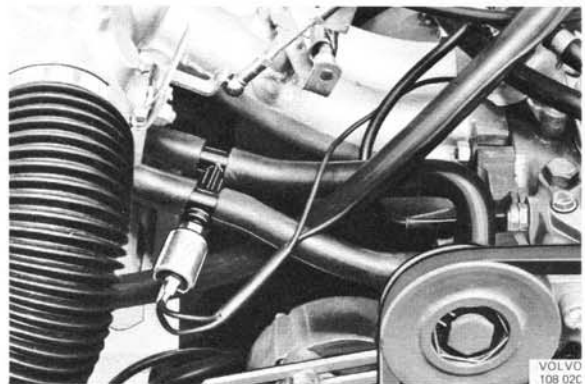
Magnetventil, Einbau auf Motor B 20 E
